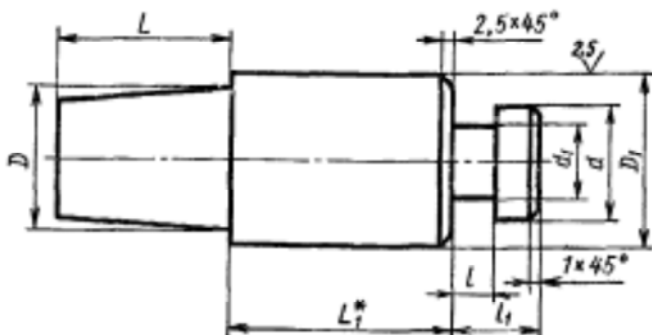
Конструкция стержней, удаляемых реечными приспособлениями
